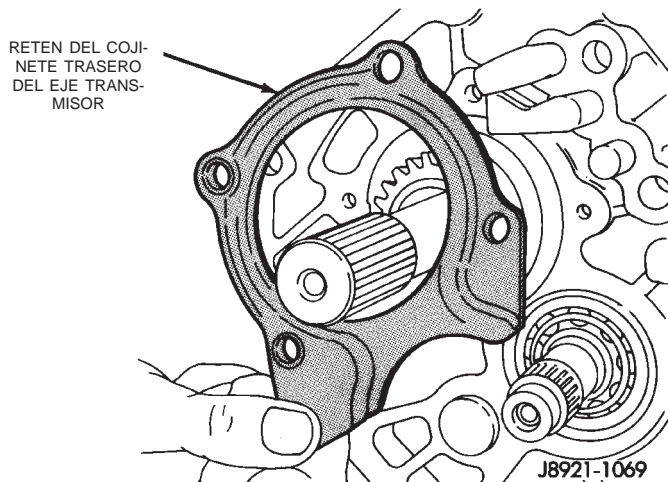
Desmontaje del retén del cojinete trasero del eje transmisor
